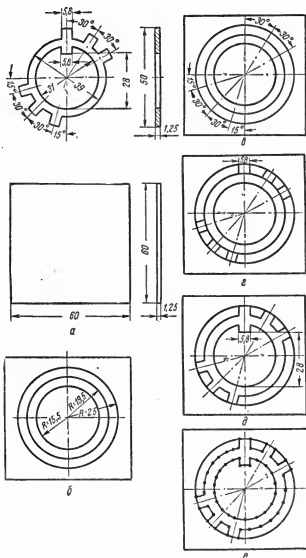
Разметка замковой шайбы к закрепительной втулке шарикоподшипника.
